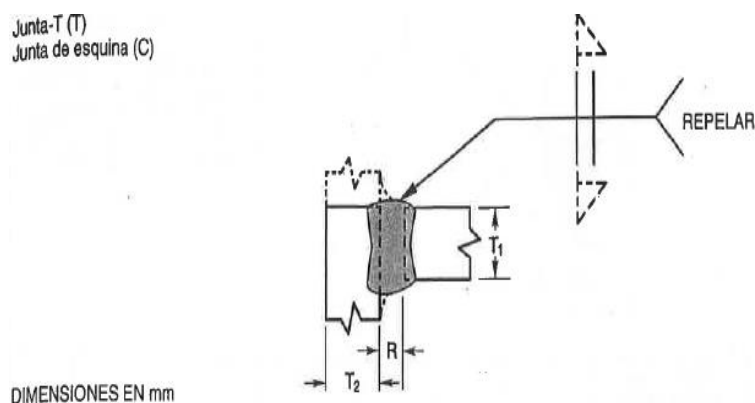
Soldadura de canal cuadrado, junta T y junta de esquina.
